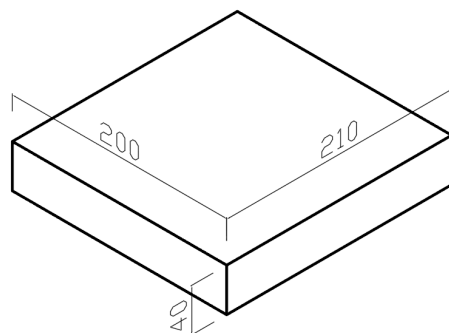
Cale en aluminium : géométrie et dimensions en mm.
